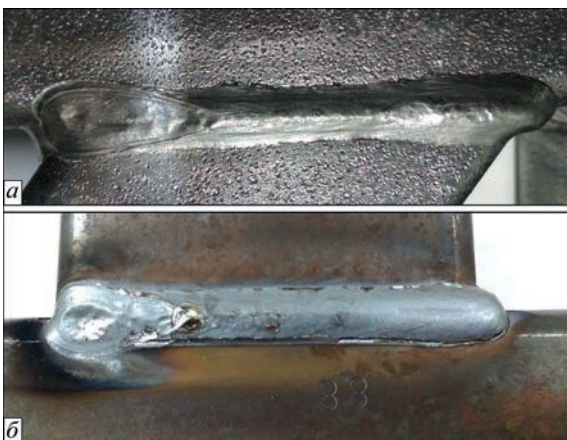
Зовнішній вигляд швів, отриманих на зразках вузла фермової конструкції з RHS елементів (стал Q235): а – звичайне GMAW; б – GMAW з гарячою присадкою
